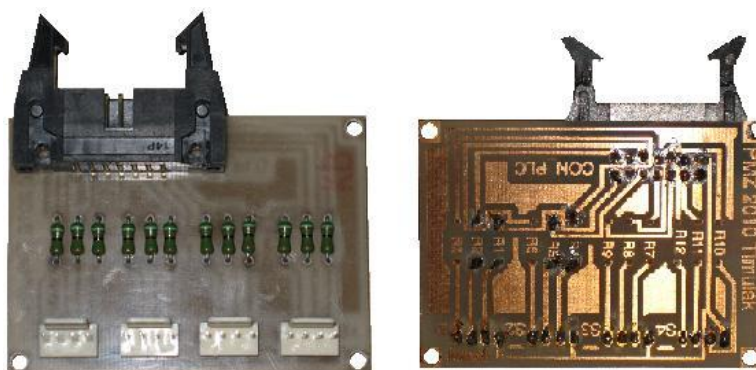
1) špatně osvětlený PCB; 2) vyleptaný PCB
